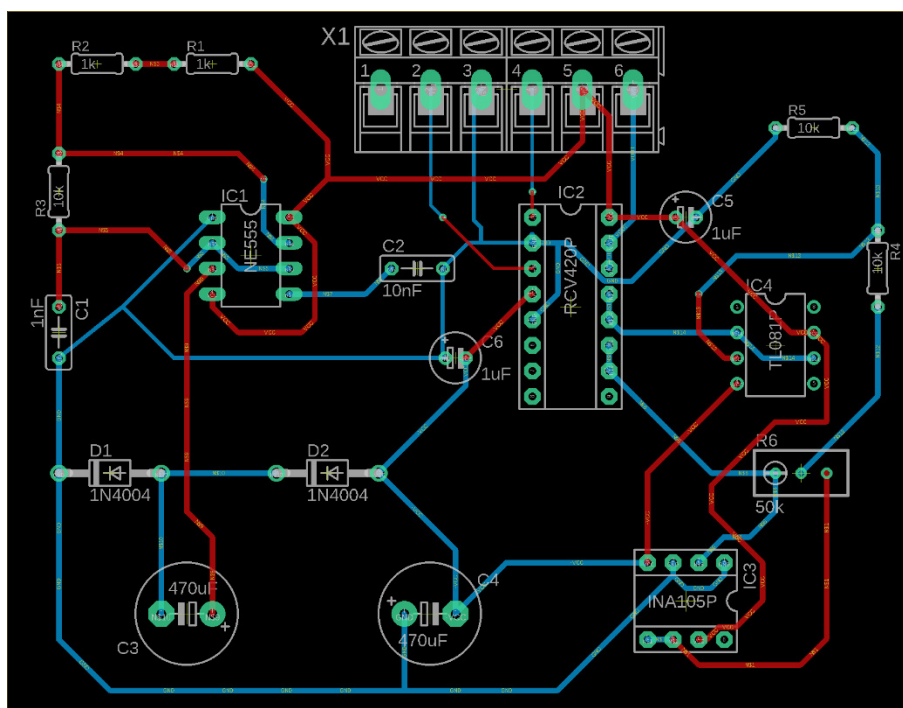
Disposición de los componentes en PCB y ruteado de pistas
